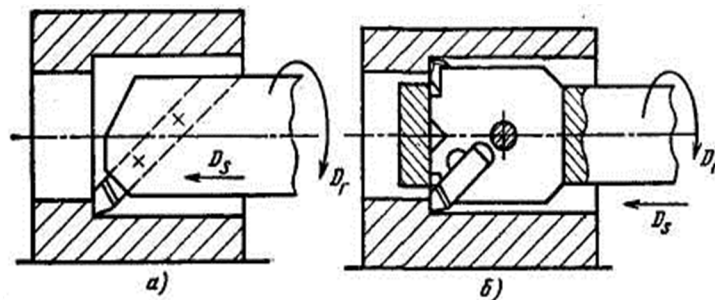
Схема растачивания отверстий резцом и плавающим блоком
